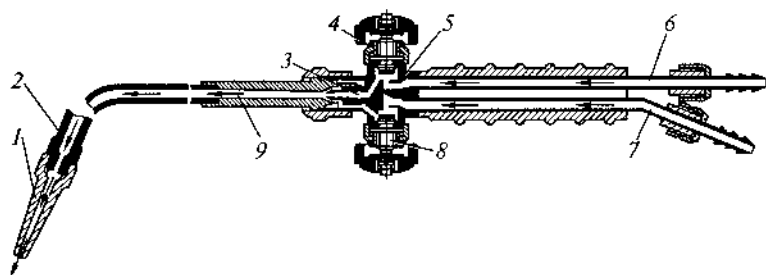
Схема инжекторной сварочной горелки:
